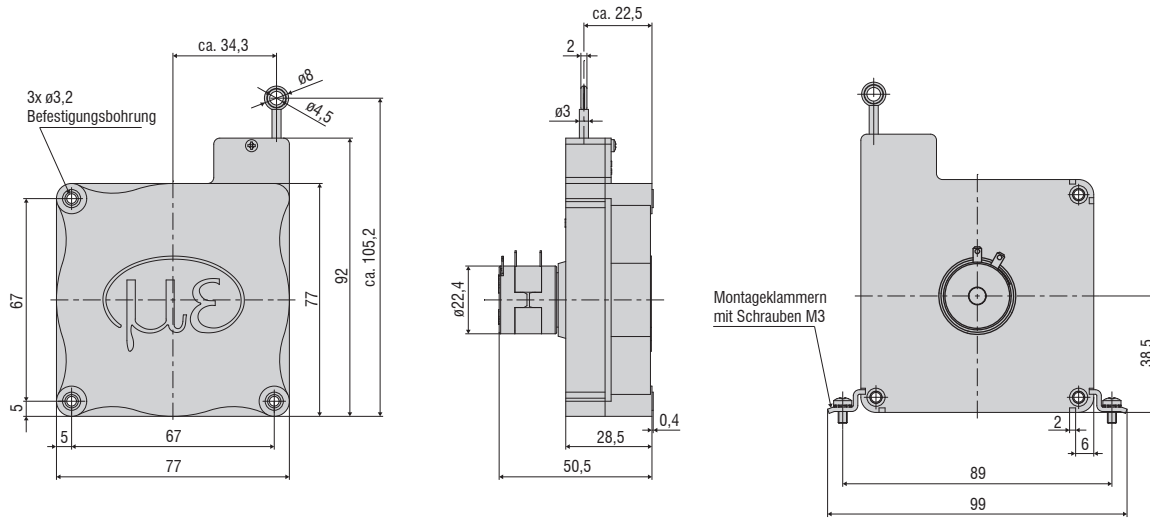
Maßzeichnung WPS-xxx-MK77-P25 mit Potentiometer, Abmessungen in mm
